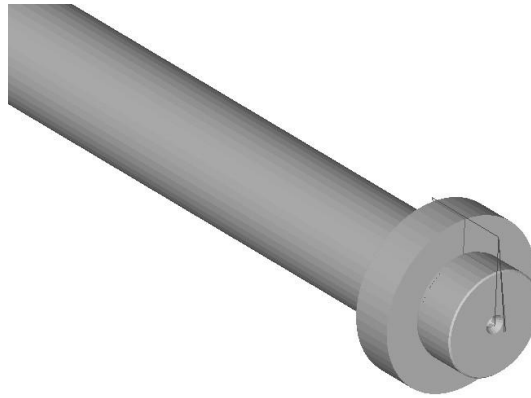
Рух інструменту при обробці лівої сторони деталі «Вал»
